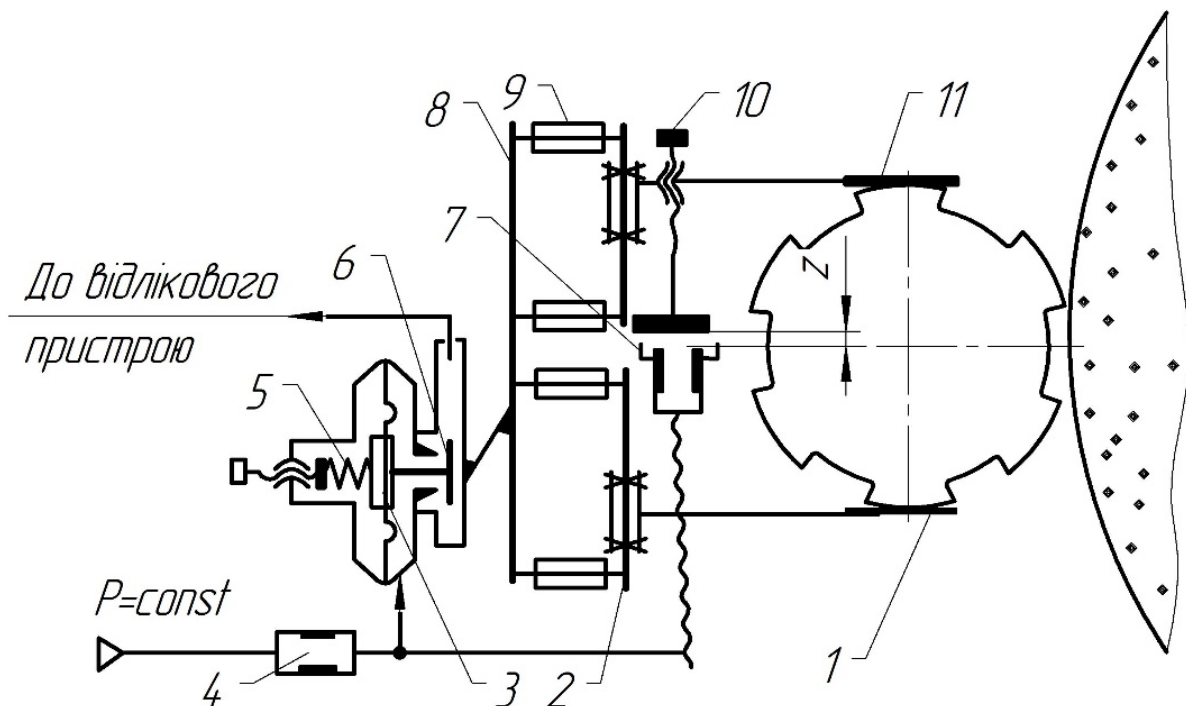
Вимірювальний пристрій з блокувальним клапаном
